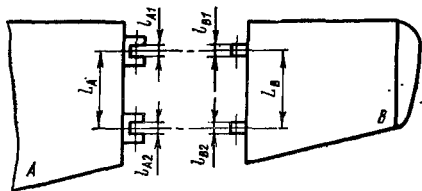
Схема увязки стыка центра (A) и ОЧК (B)
